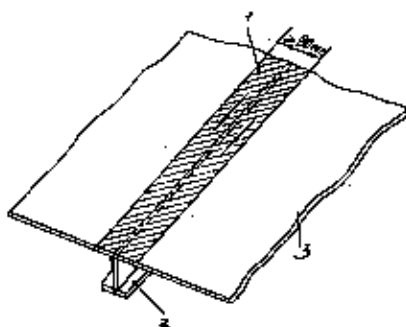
Схема упрочнения околошовной зоны с противоположной стороны приварки тавровой балки:
